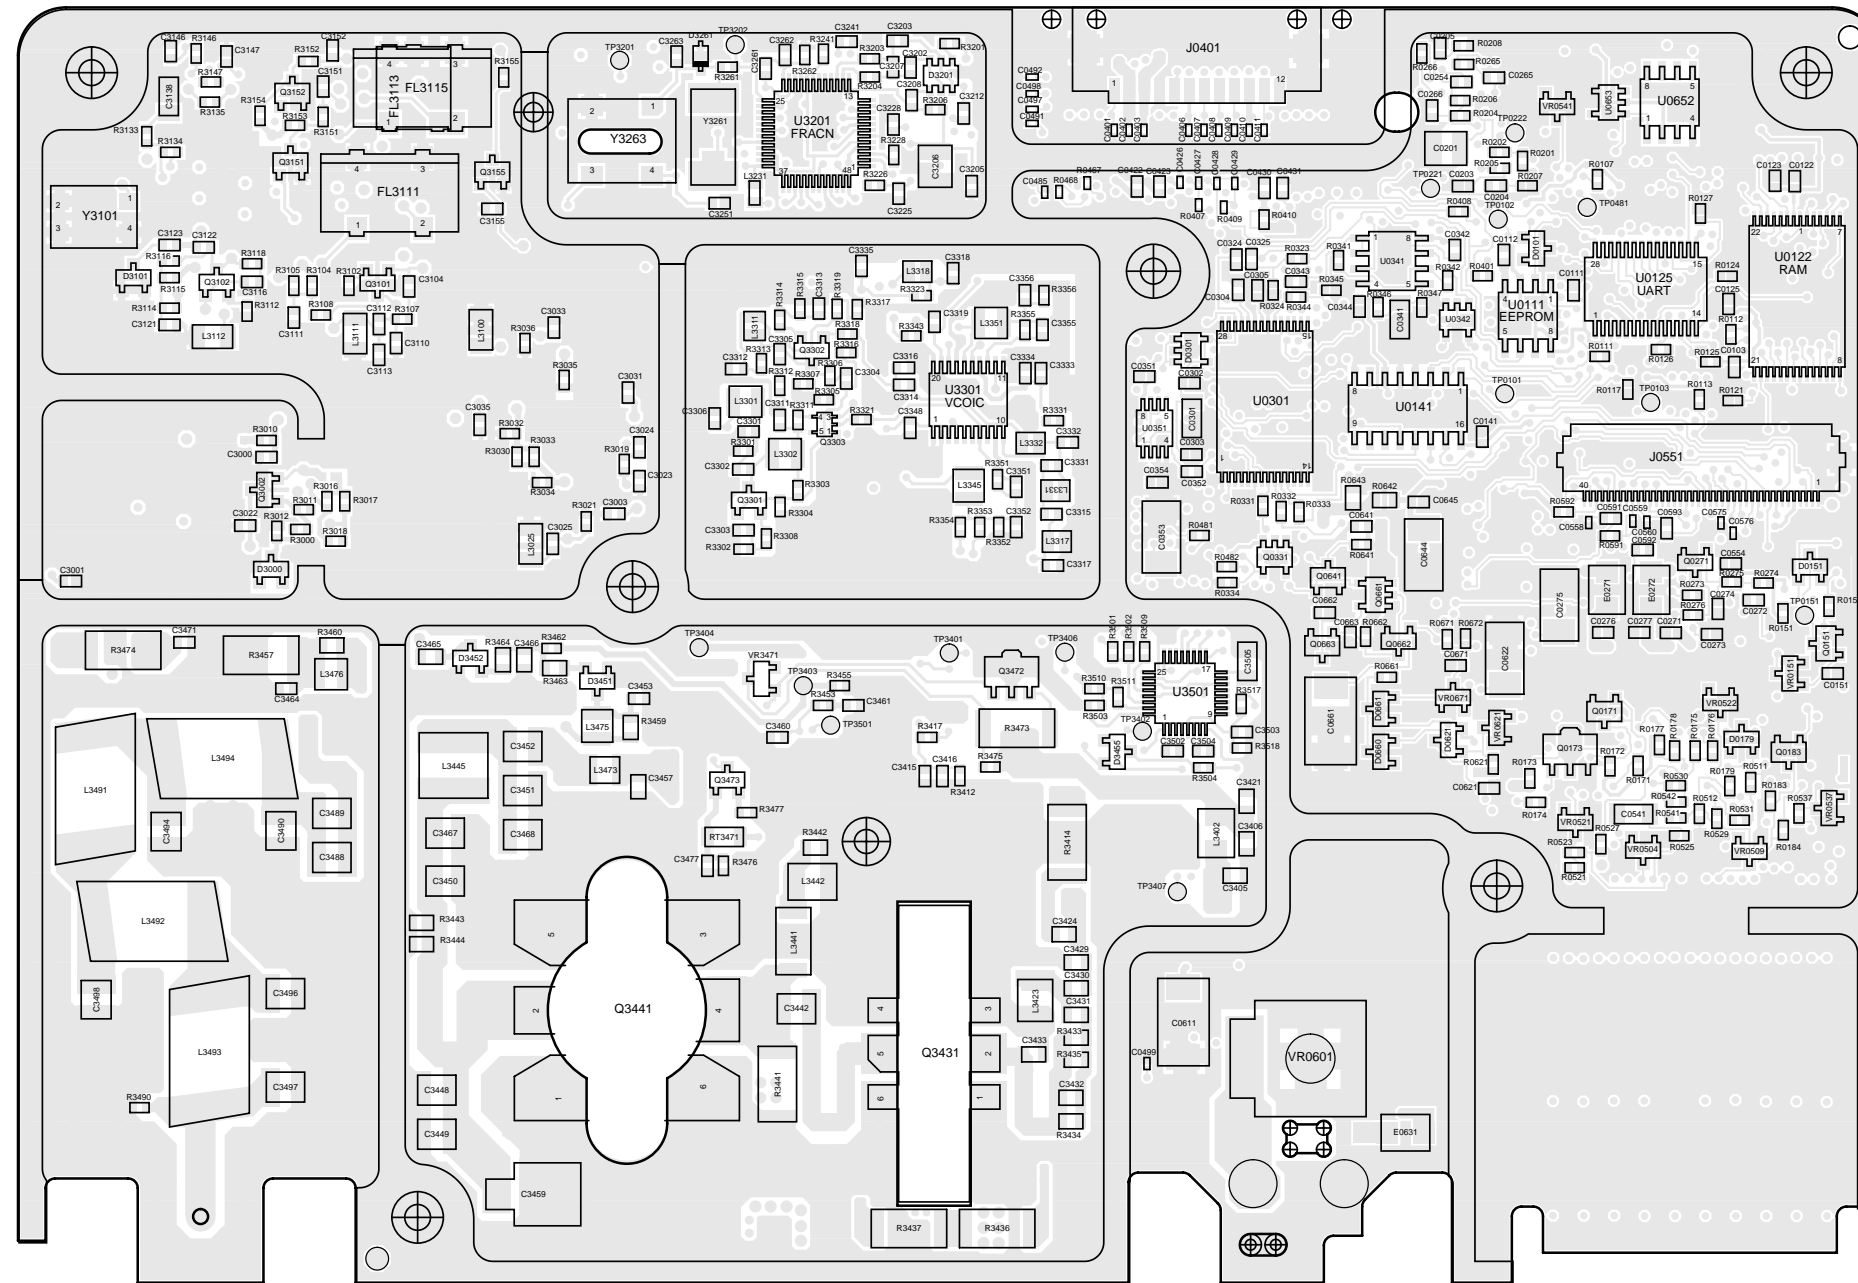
PCB del lado inferior de la tarjeta principal de VHF (136-174MHz)
